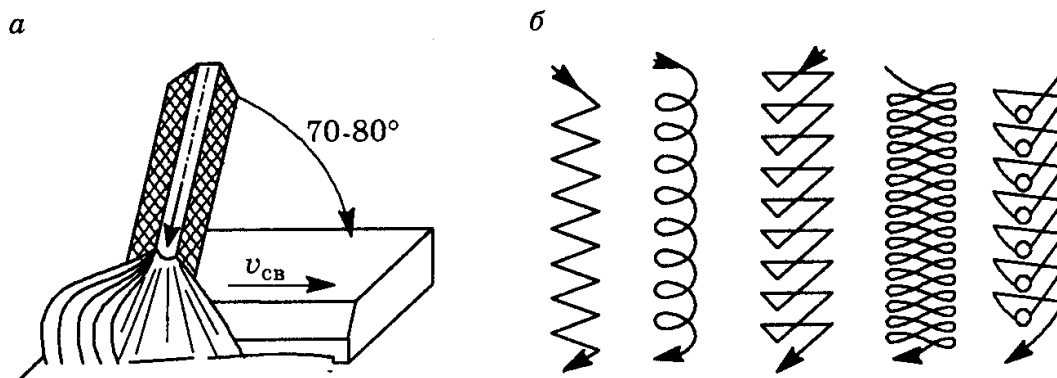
Положение (а) и поперечное движение (б) электрода при сварке нижних стыковых швов
